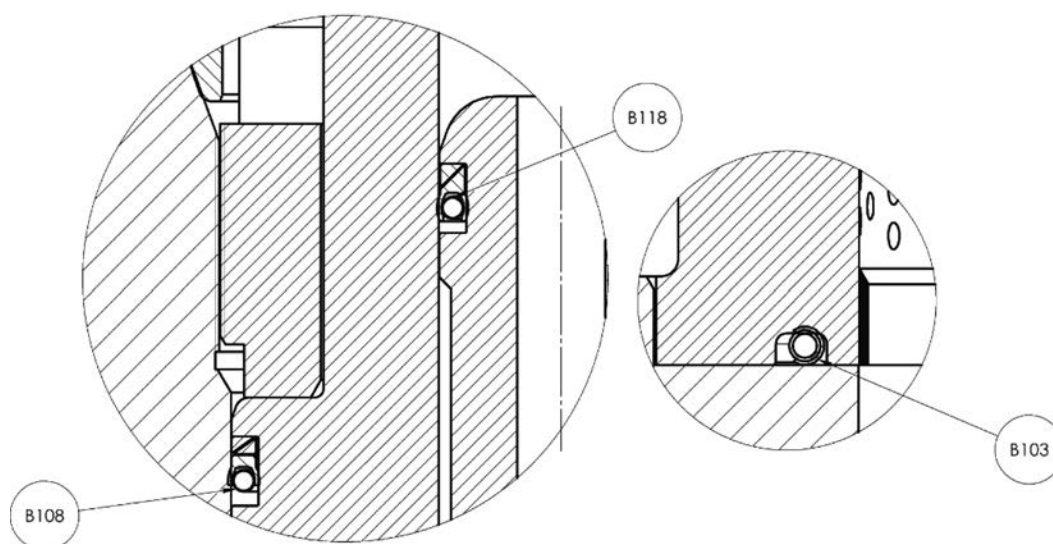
Монтаж уплотнений и прокладки для исполнения „поток на открытие“
